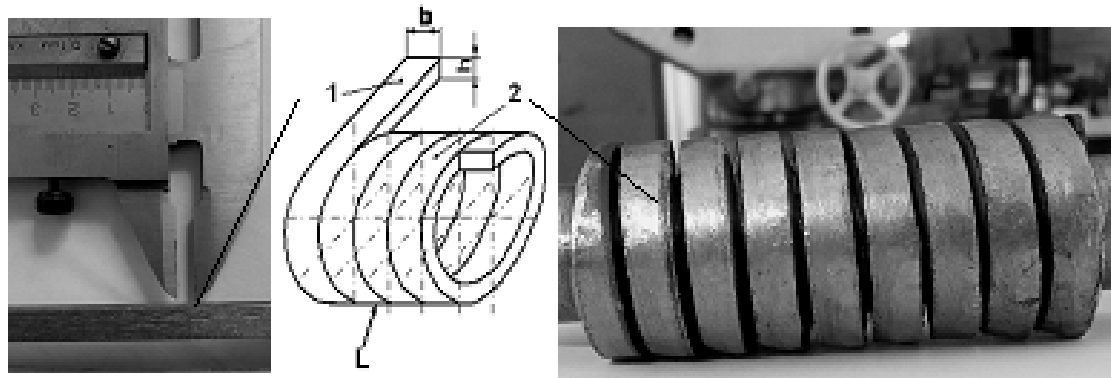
Навивання прутка 1 по прямолінійній твірній L циліндричної поверхні 2 (а – початковий прямолінійний пруток; б – схема операції; в – навитий пруток)
